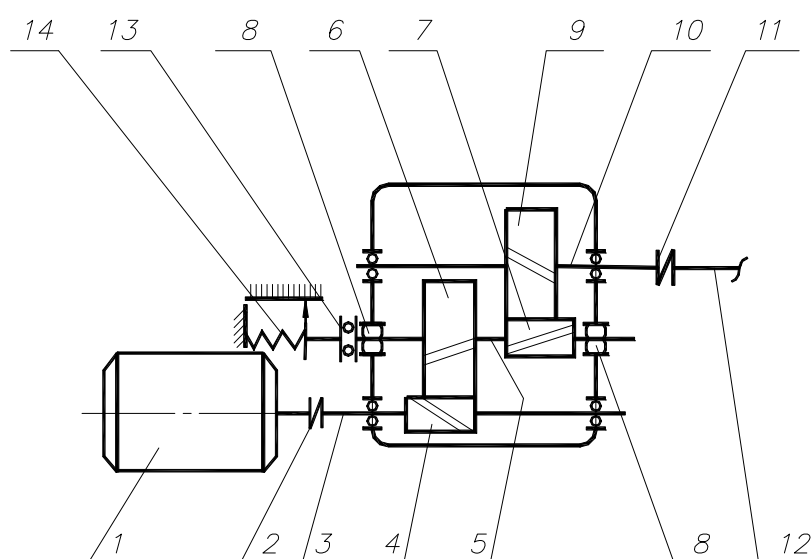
Схема устройства для измерения крутящего момента на базе двухступенчатого редуктора с косозубыми колесами
